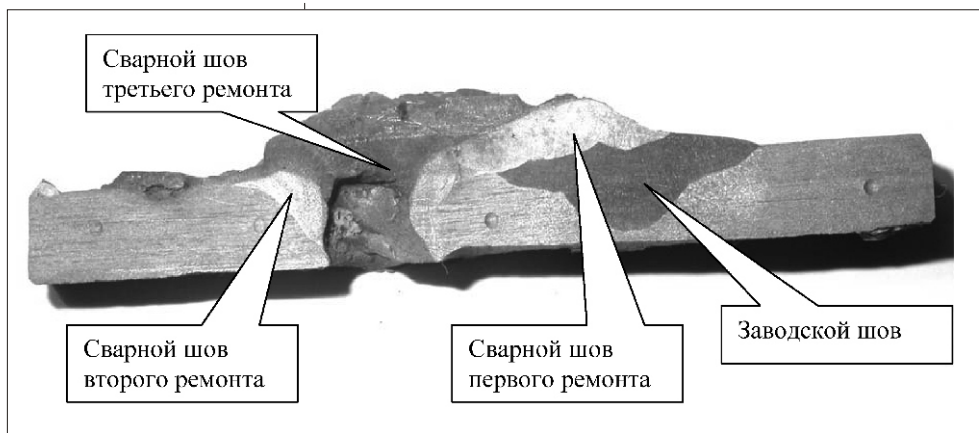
Поперечное сечение ремонтного сварного шва
